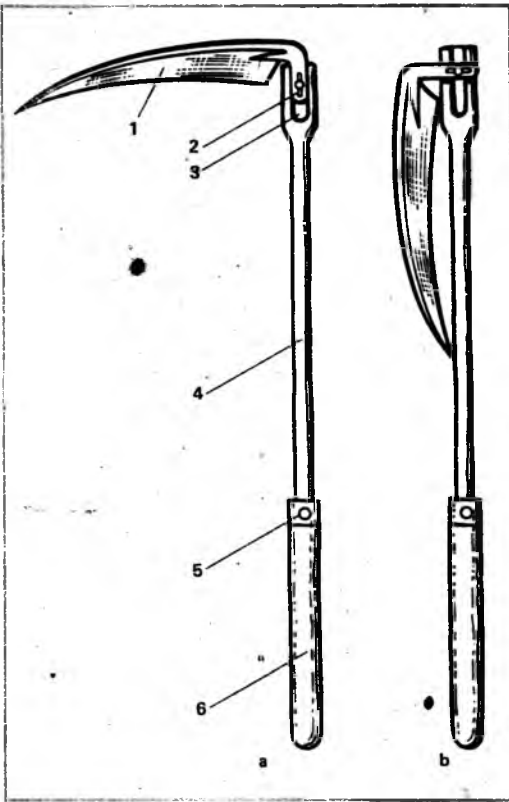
Коса-серпан: а — рабочее положение; б — транспортное положение; 1 — нож косы; 2 — гайка-барашек; 3 — паз удлинителя; 4 — удлинитель; 5 — колпачок; 6 — черенок
